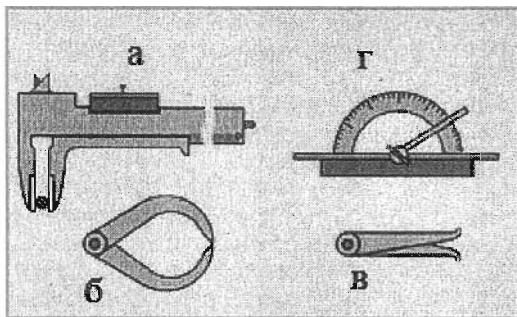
Измерительный инструмент: а – штангенциркуль; б – кронциркуль; в – нутромер; г – самодельный угломер
